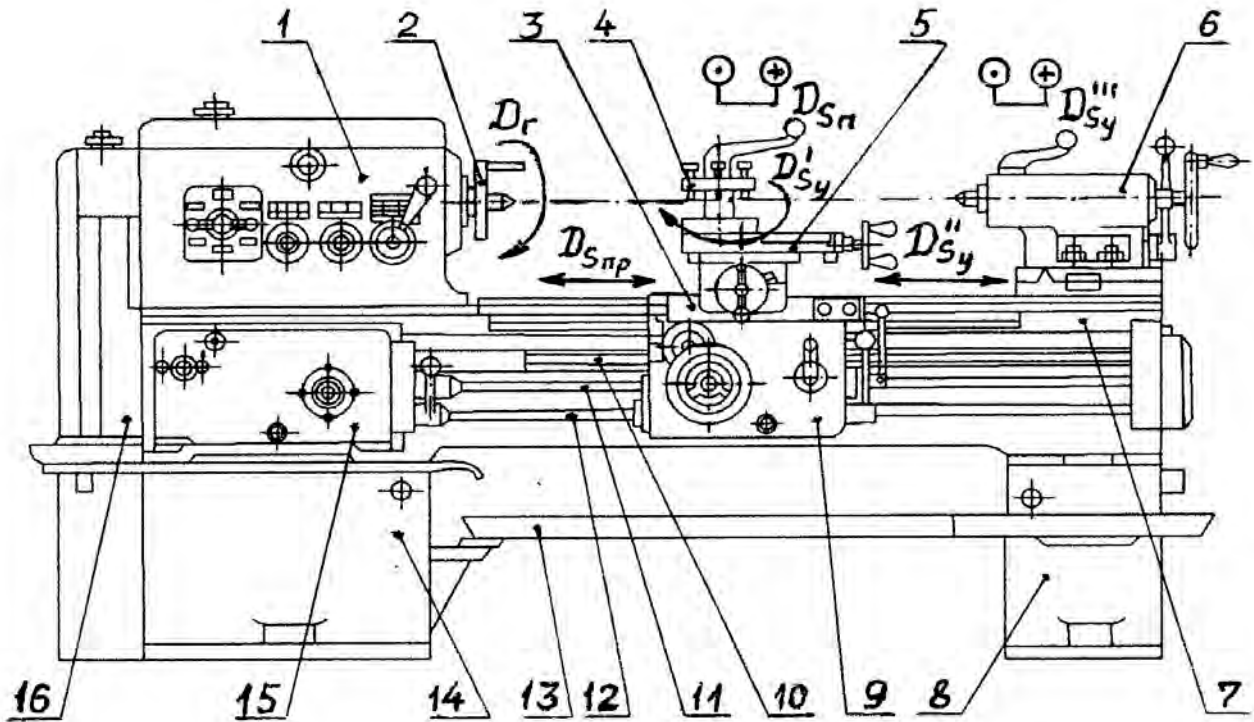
Схема токарно-винторезного станка 16К20 с указанием движений на нем: 1 — передняя бабка с коробкой скоростей и рукоятками управления ею; 2 — установленная на шпинделе поводковая шайба с центром (приспособление); 3 — суппорт; 4 — резцедержатель (приспособление); 5 — верхние поворотные салазки; 6 — задняя бабка; 7 — станина; 8 — правая тумба, в которой размещена насосная станция подачи СОЖ; 9 — фартук суппорта с органами управления движениями подач; 10 — ходовой винт; 11 — ходовой вал; 12 — вал с рукоятками управления включением-выключением и направлением (реверсом) вращения шпинделя; 13 — поддон (корыто); 14 — левая тумба; 15 — коробка подач с органами управления; 16 — гитара сменных зубчатых колес, служащая для настройки на шаг нарезания специальных резьб;  $D_r$  — главное движение, осуществляемое вращением шпинделя с заготовкой;  $D_{Snp}$  — движение продольной подачи суппорта (каретки);  $D_{Sn}$  — движение поперечной подачи салазок;  $D_{Sy}'$  — установочное движение подачи в виде фиксированного поворота верхних салазок;  $D_{Sy}''$  — установочное движение подачи в виде фиксированного перемещения задней бабки вдоль направляющих станины;  $D_{Sy}'''$  — установочное движение подачи в виде фиксированного поперечного перемещения задней бабки.
